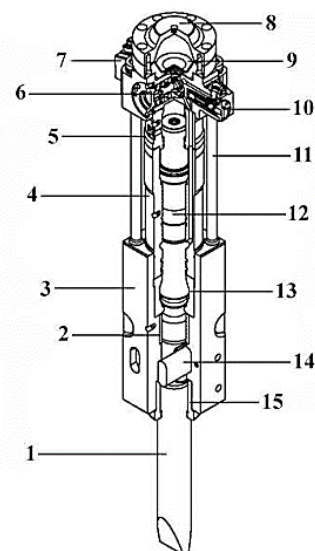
Пристрій мембранного гідромолота: 1 – робочий інструмент; 2 – верхня втулка; 3 – передня головка; 4 – циліндр; 5 – корпус ущільнення; 6 – втулка; 7 – корпус клапана; 8 – акумулятор; 9 – мембрана; 10 – робочий клапан; 11 – стяжний болт; 12 – поршень; 13 – упорне кільце; 14 – штифт робочого інструменту; 15 – втулка робочого інструменту [1]
